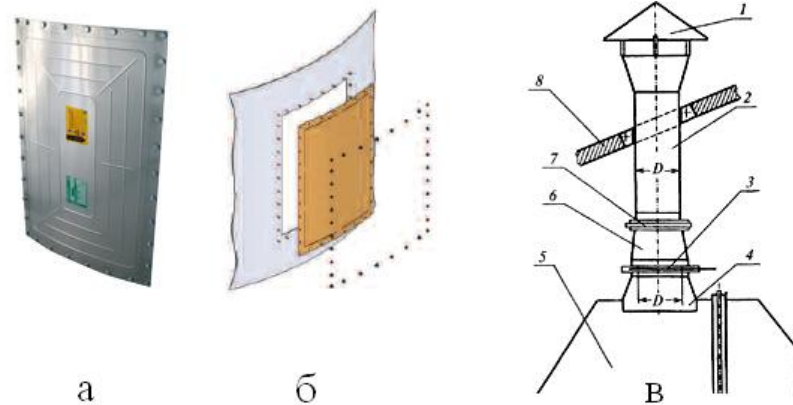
Вибухорозрядні пристрої: вибухорозрядна мембрана EX-GO-VENT прямокутної форми (а) та її монтажу (б); вибухорозрядний пристрій шибєрного типу: 1 – захисний ковпак; 2 - вертикальна труба з дифуззором; 3 – вибухорозрядний пристрій шибєрного типу; 4 - вхідний патрубок; 5 - корпус головки норії; 6 - перехідник; 7 - хомут; 8 – укриття.
